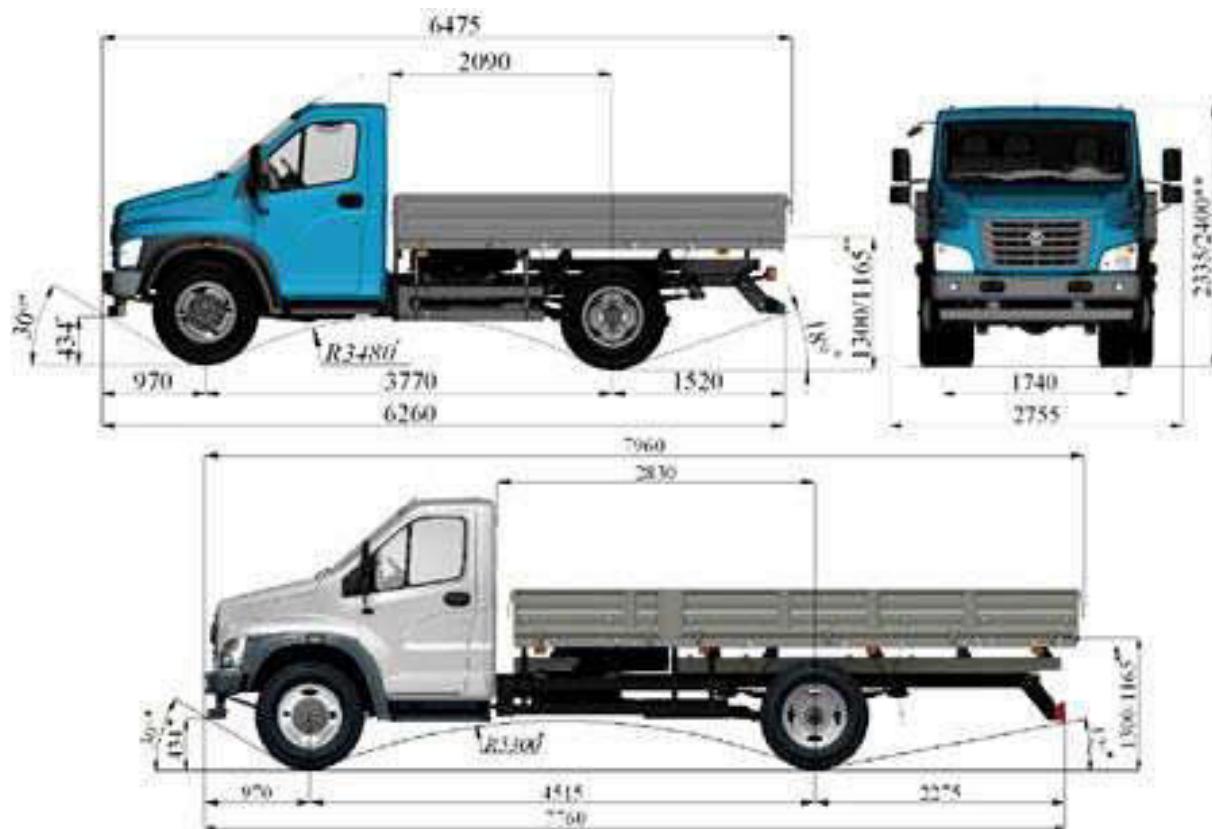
Внешний вид автомобиля “ГАЗОН НЕХТ”
